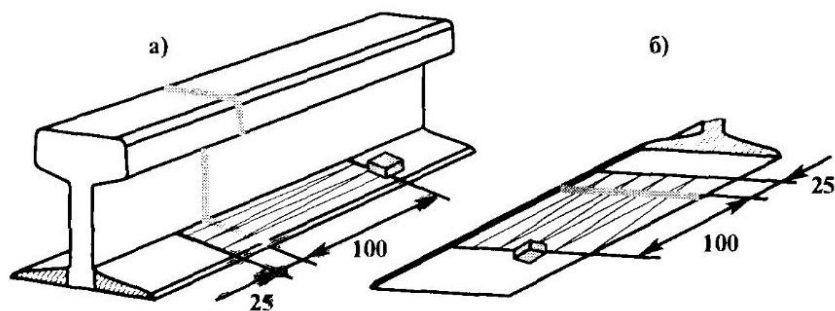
Схема прозвучивания перьев подошвы: а – сверху и б – снизу в зоне сварного стыка.
